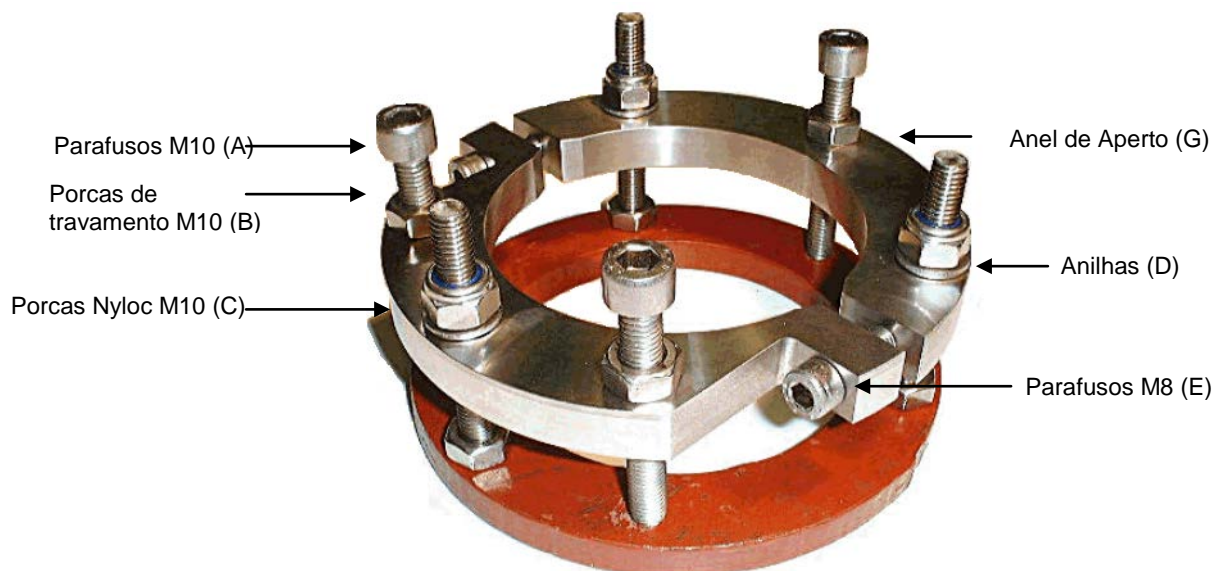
Anel de Aperto Ajustável montado e instalado na Placa de Fixação
